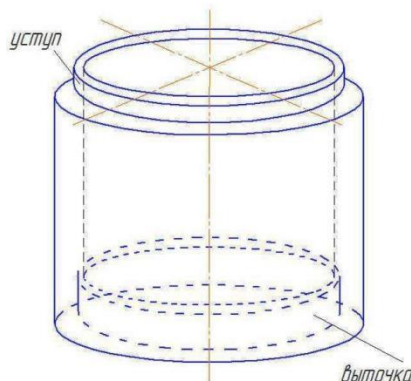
Изометрия керамического фильтра воздушного компрессора.
